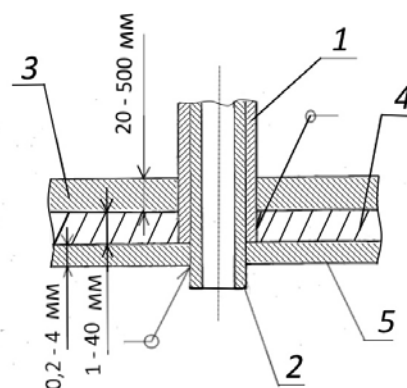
Соединение биметаллической трубки с трубной решеткой: 1 – труба из нержавеющей стали; 2 – вкладка в трубу из циркония; 3 – трубная решетка из нержавеющей стали; 4 – защитный промежуточный слой из нержавеющей стали; 5 – циркониевая накладка
